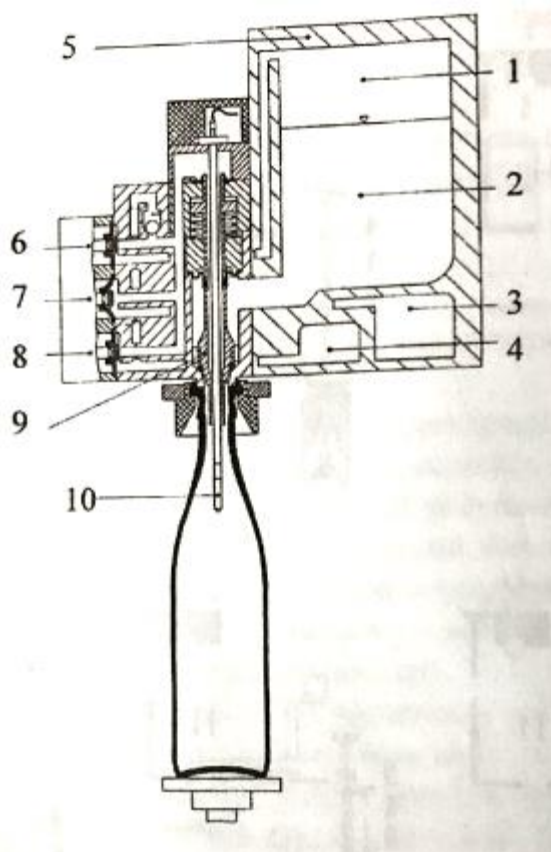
Схема фасувального пристрою машини ZMS: 1 – камера нагнітання газу CO_2 ; 2— камера для продукції; 3 – вакуумна камера; 4 – камера для зворотнього газу; 5 — кільцевий резервуар; 6 – циліндр для керування подачею газу нагнітання; 7- циліндр для керуванням створенням вакууму; 8— циліндр для керування переміщенням зворотного газу; 9 — рідинний клапан; 10 - зонд;
